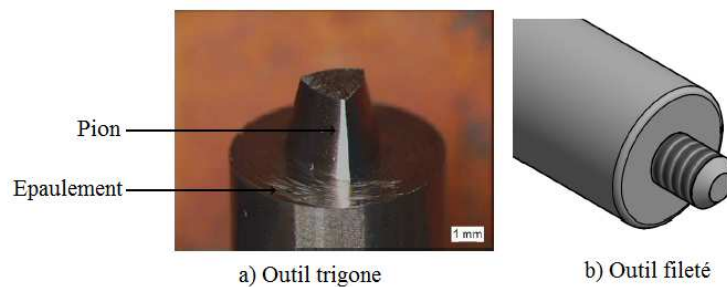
Outil de soudage FSW (Trigone et fileté) [8].
